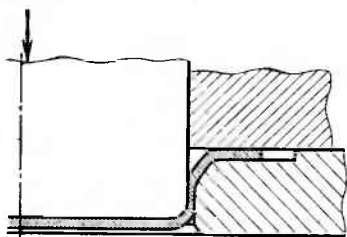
Схема вытяжки на конической матрице (с конструктивно принятыми параметрами) с плоским складкодержателем
